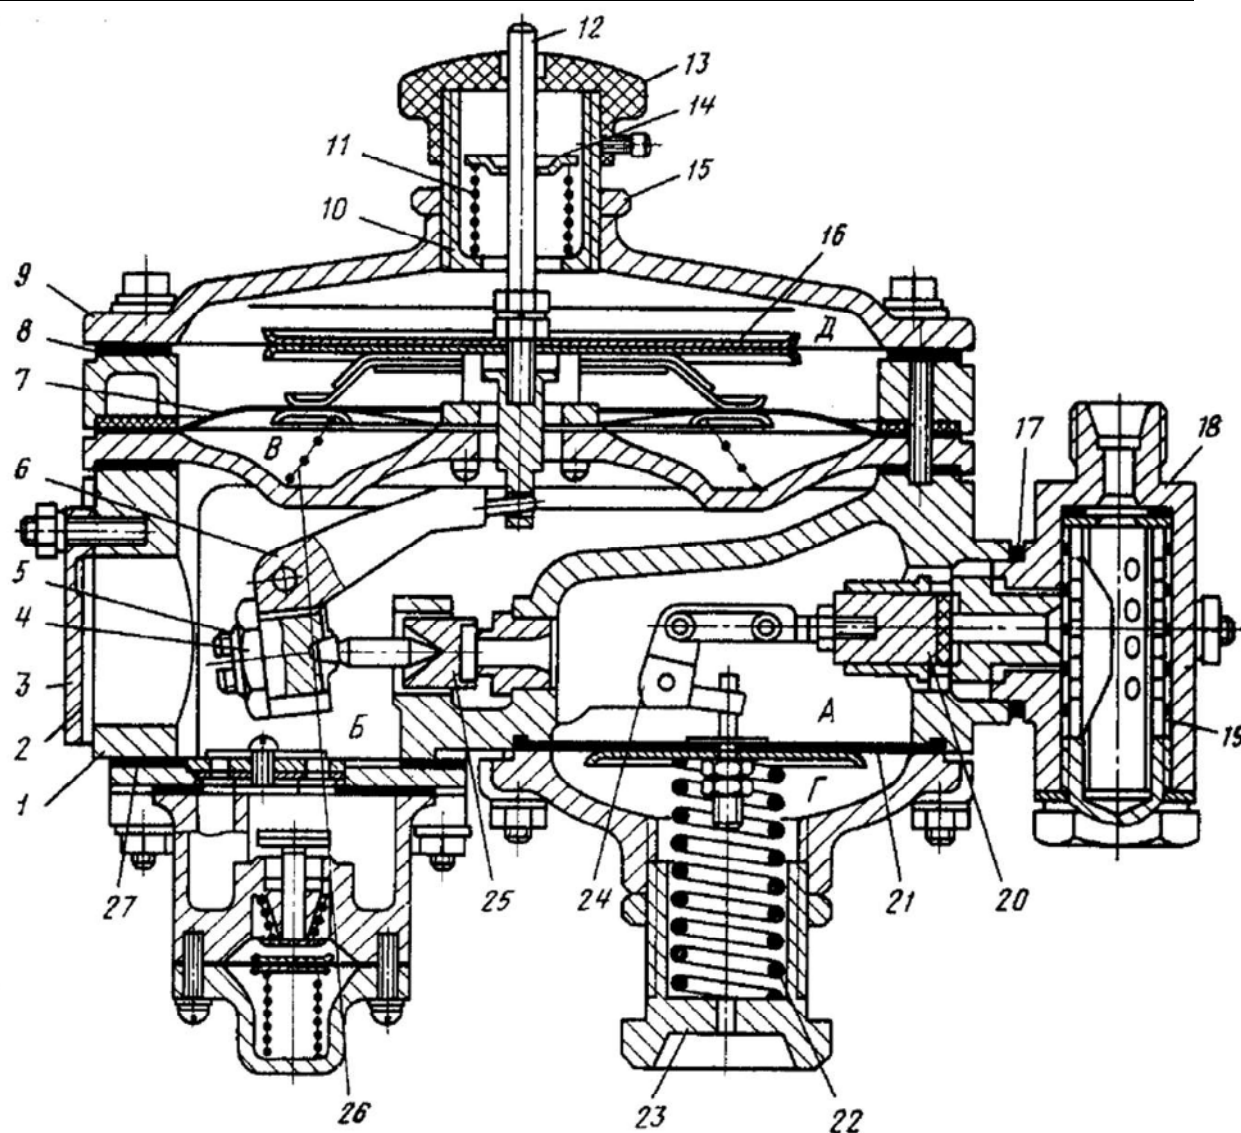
Газовый редуктор низкого давления: А - полость первой ступени; Б - полость второй ступени; В - полость разгрузочного устройства; ГД- полости атмосферного давления; 1 - корпус газового редуктора; 2 - прокладка; 3- крышка; 4 - контргайка регулировочного винта; 5 - регулировочный винт клапана низкого давления; 6 - рычаг диафрагмы низкого давления; 7 - разгрузочная диафрагма; 8 -
